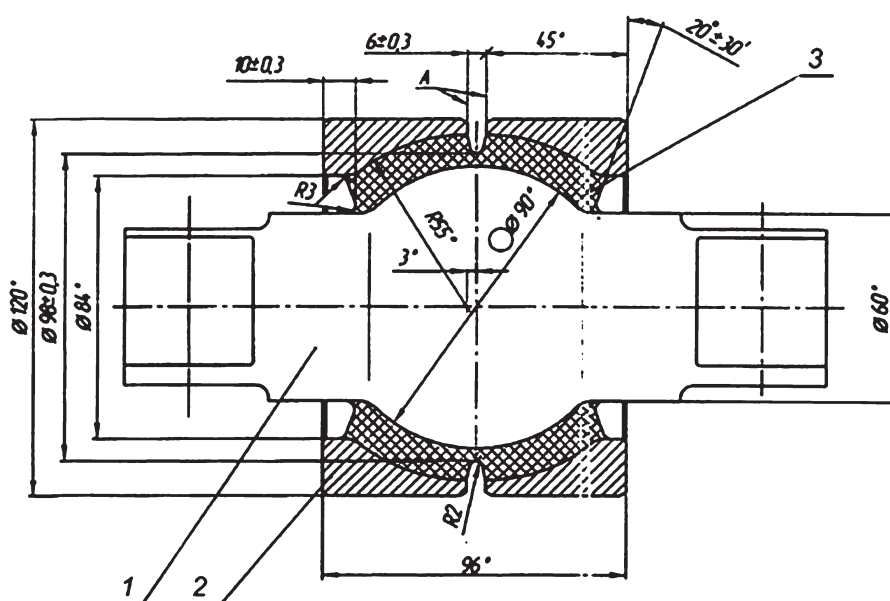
Сферический резинометаллический шарнир: 1 – внутренняя обойма; 2 – наружная обойма; 3 – резиновая втулка
